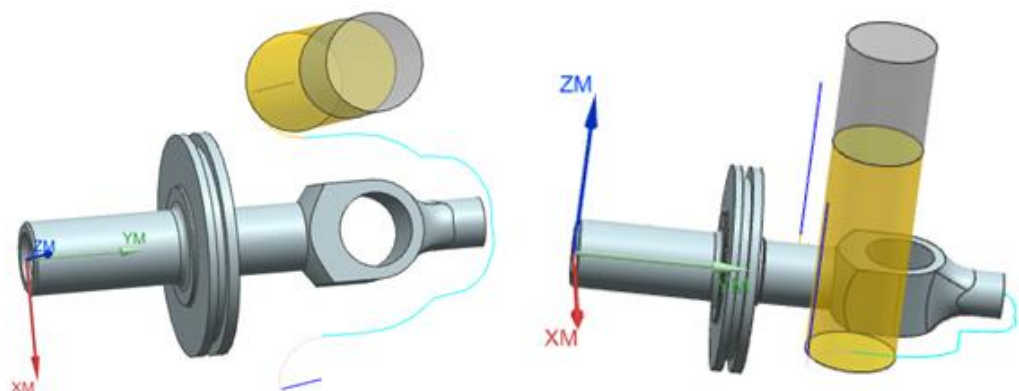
Ескіз обробки для фрезерного переходу
